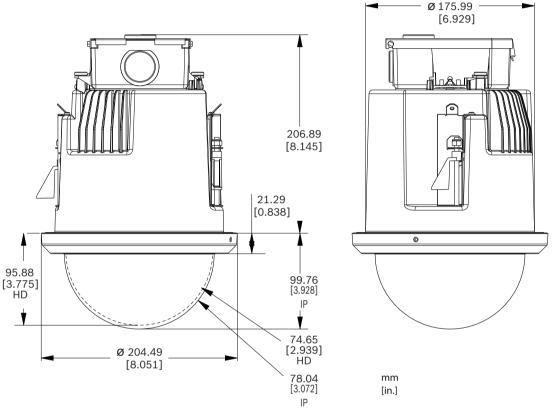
Dimensiones de AUTODOME 7000: montaje en techo
